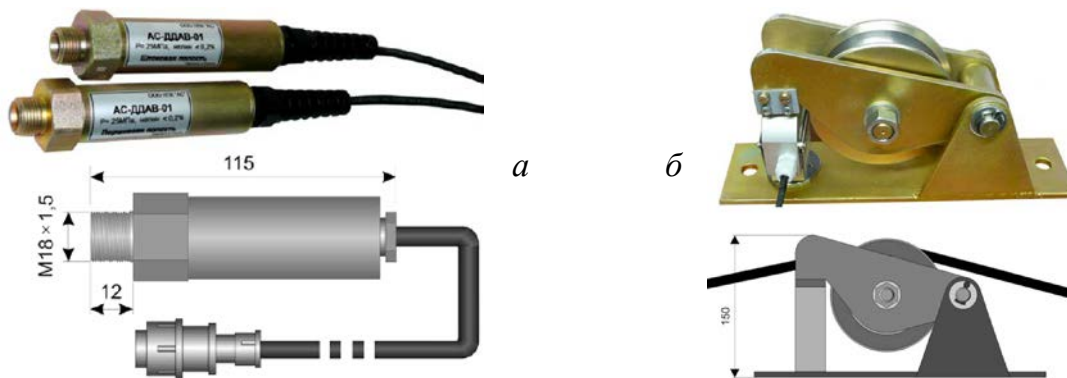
Внешний вид и габариты датчиков грузового момента:
